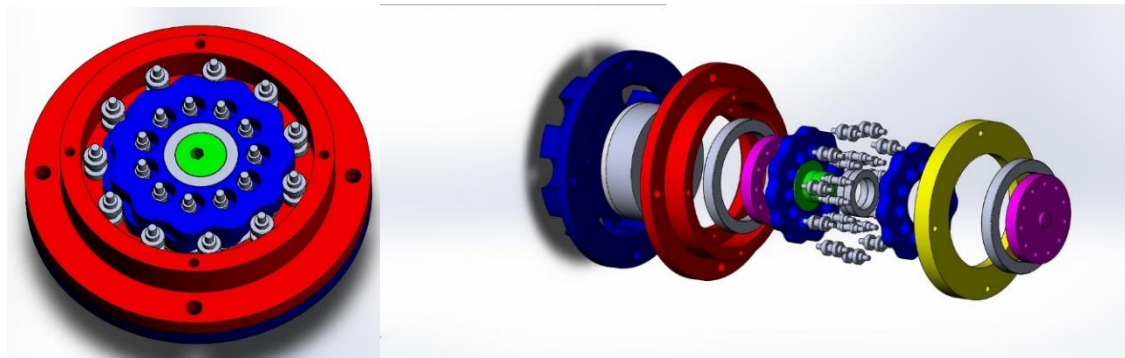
Вид редуктора без выходного звена и с разнесенными элементами
